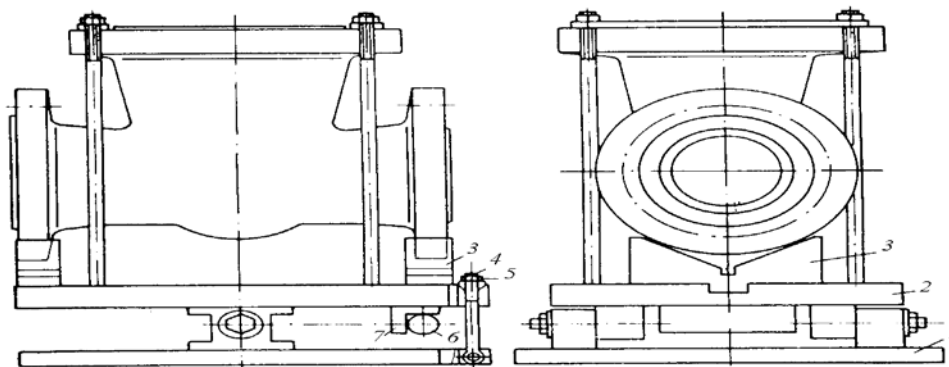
Приспособление для проточки зеркал клиновых задвижек:
